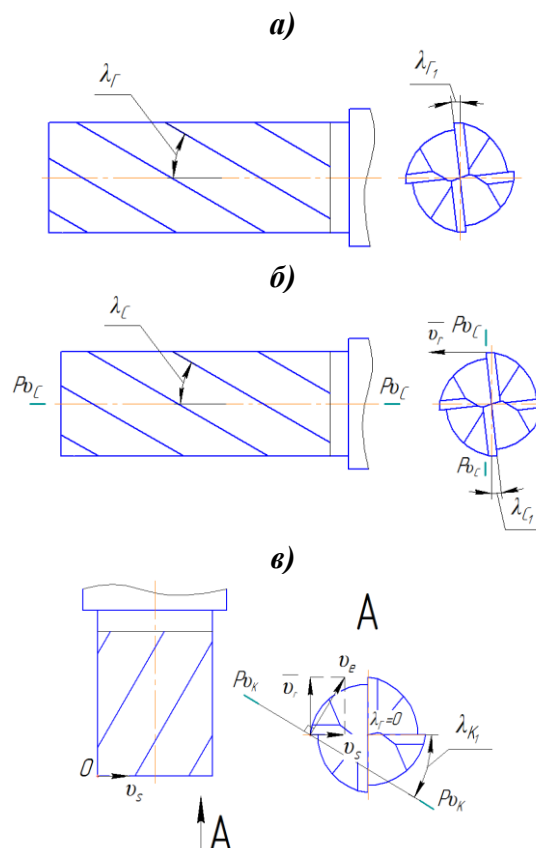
Схема для определения угла наклона режущей кромки инструмента в инструментальной (а), статической (б) и кинематической (в) системах координат
